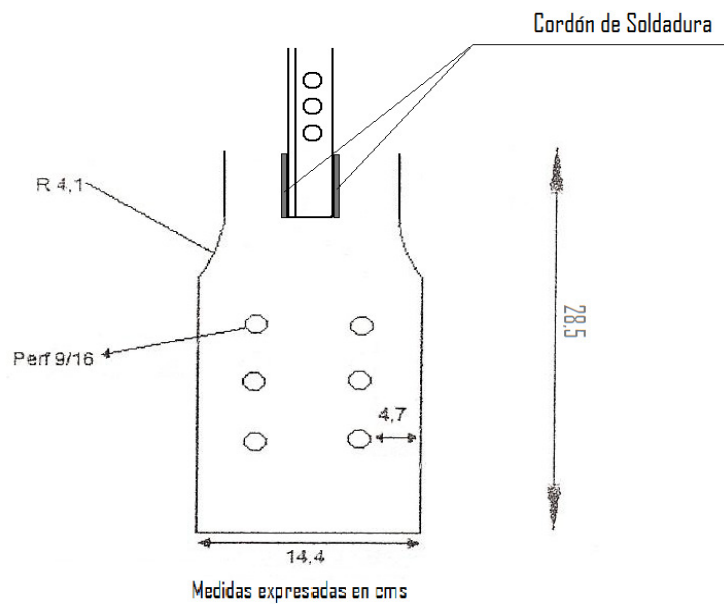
Geometría de platina parte inferior después de soldada.
